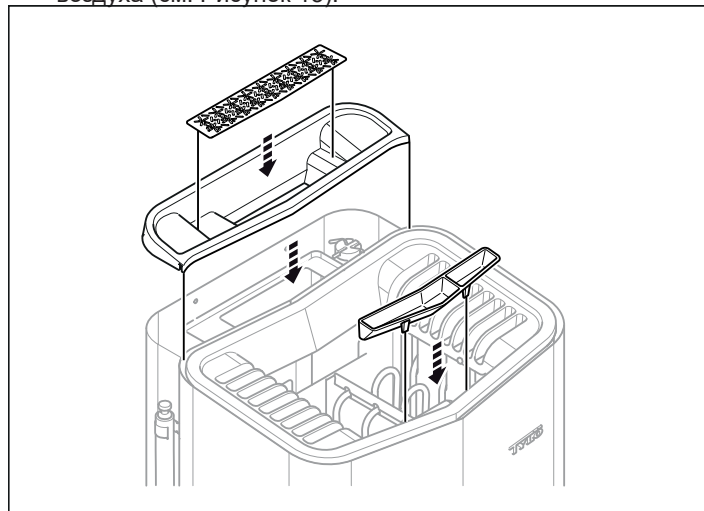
Установка крышки для резервуара для воды, решетки для трав и держателя для ароматизатора/увлажнителя воздуха
